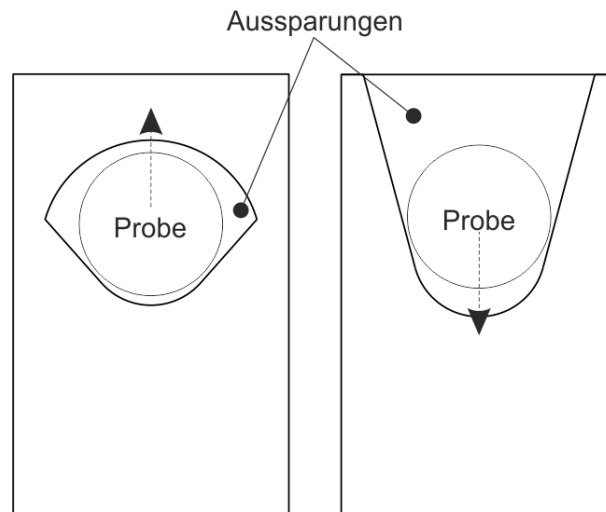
Frontansicht Probenhalterungen mit den Aussparungen zur Aufnahme und Ausrichtung der Proben
